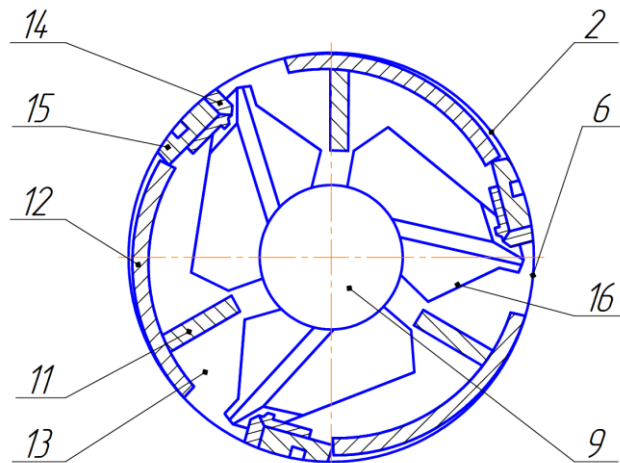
Ротор: 1 – лопаті; 12 – стінка; 13 – диск; 14 - било; 15 – блок поворотний; 16 - напрямні.
